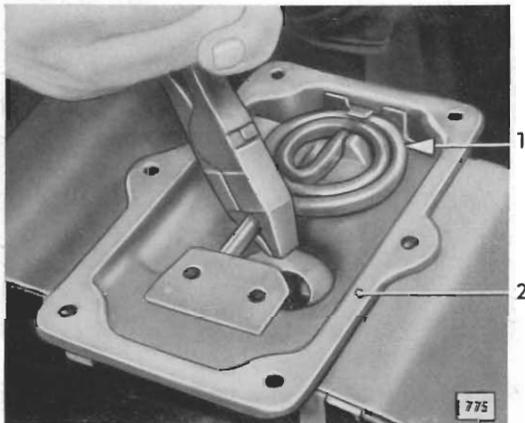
Anschlagfeder für Rückwärtsgang herausnehmen
